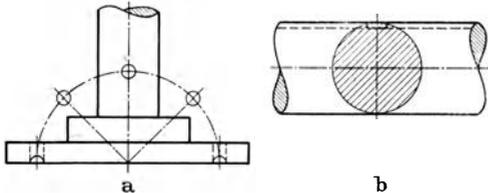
Im Werkstück eingezeichnete Schnitte oder Ansichten.
